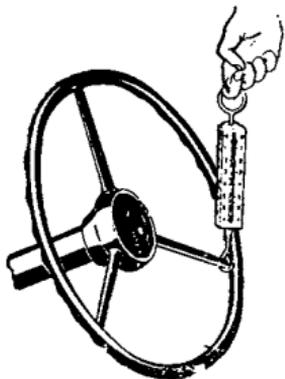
Проверка затяжки подшипников червяка с помощью динамометра
